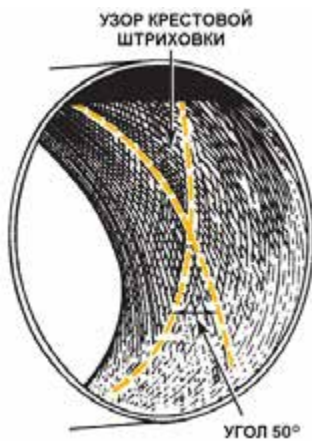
Штриховка перекрестными штрихами стенок цилиндров позволяет удерживать масляную пленку на стенках цилиндра, необходимую для смазки поршневых колец, в то же время подобная штриховка остается газонепроницаемой.
